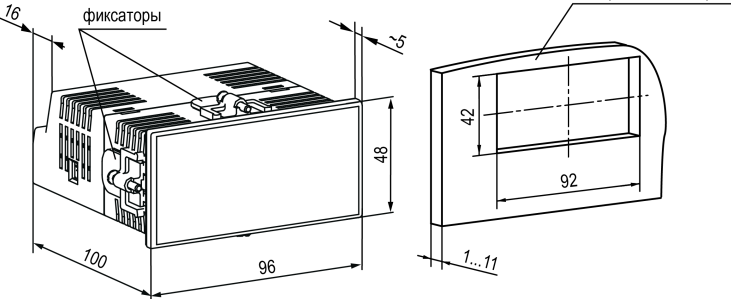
Габаритные размеры корпуса Щ2 и монтажного отверстия в щите
